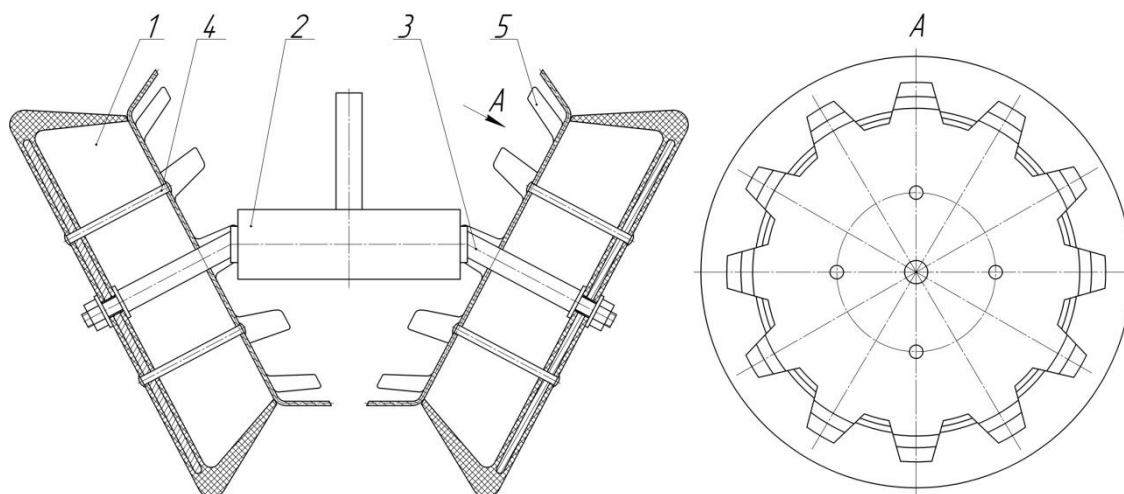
Загортаючий робочий орган картоплесадильної машини:
